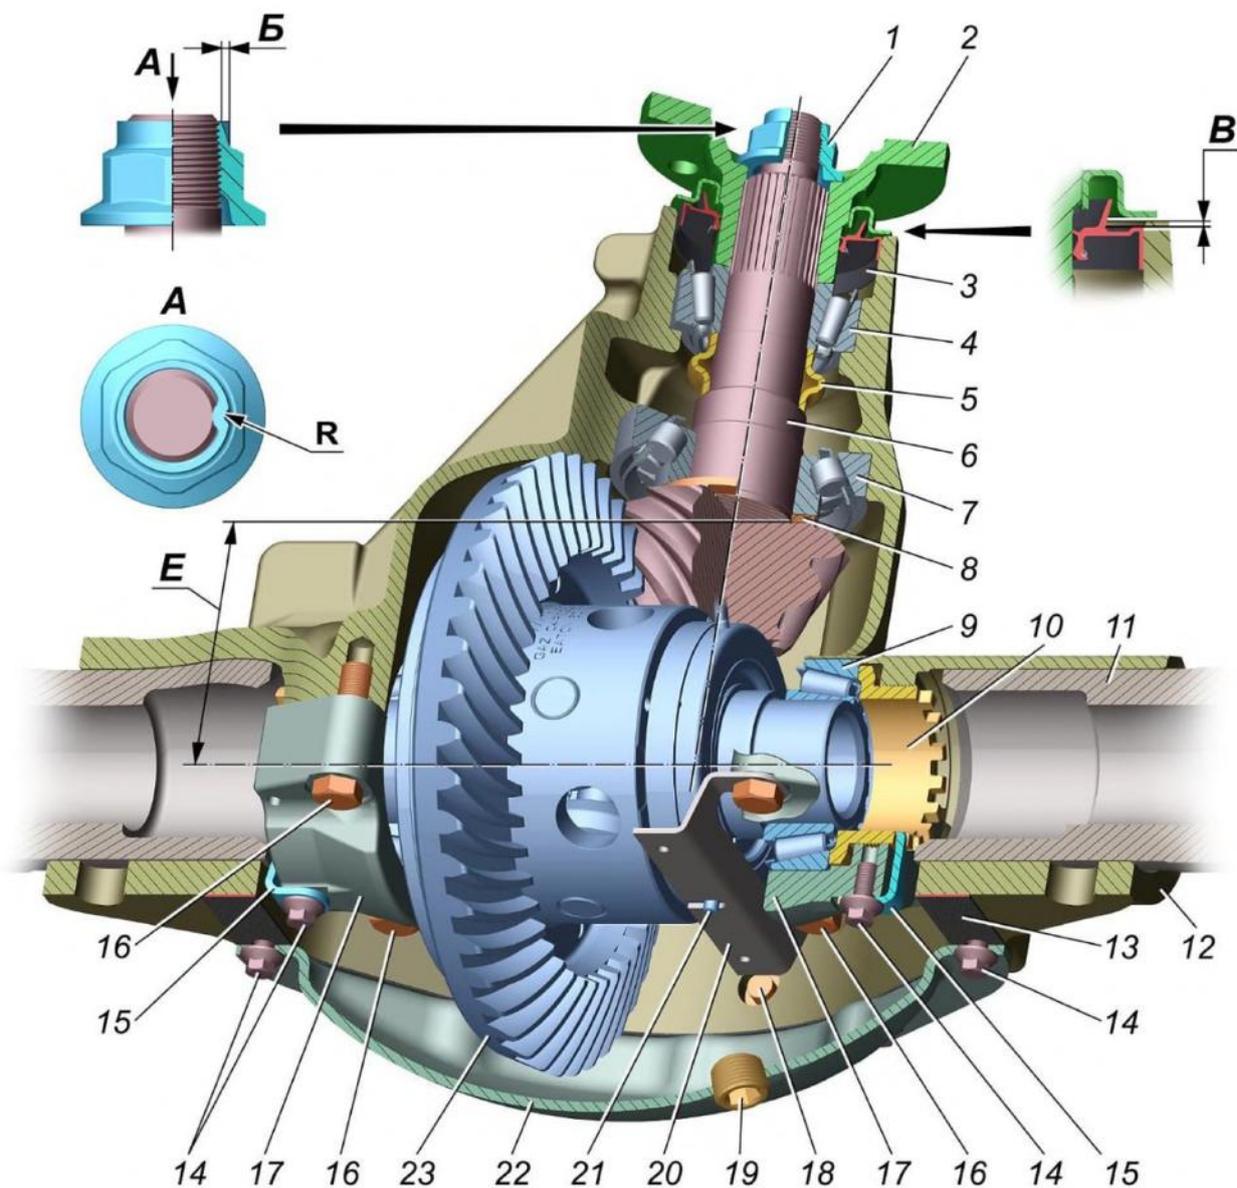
Редуктор заднего моста с блокируемым дифференциалом: 1 - гайка; 2 - фланец ведущей шестерни; 3 - манжета; 4,7,9 - подшипники; 5 - распорная втулка; 6 - ведущая шестерня; 8 - регулировочное кольцо; 10 - гайка подшипников дифференциала; 11 - кожух полуоси; 12 - картер заднего моста; 13 - прокладка; 14,16 - болты; 15 - стопорная пластина; 17 - крышка подшипника дифференциала; 18 - пробка магнитная; 19 - пробка маслозаливного отверстия; 20 - пластина стопорная; 21 - штифт обоймы электромагнита; 22 - крышка картера; 23 - блокируемый дифференциал с ведомой шестерней
